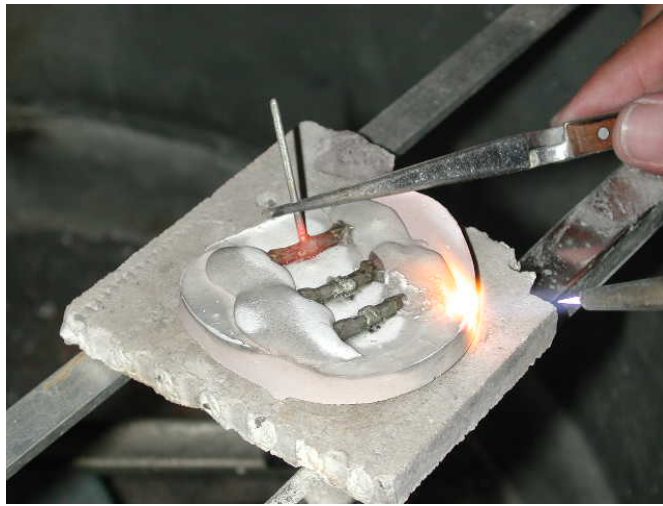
Aplicación de soldadura marca DENTORIUM
